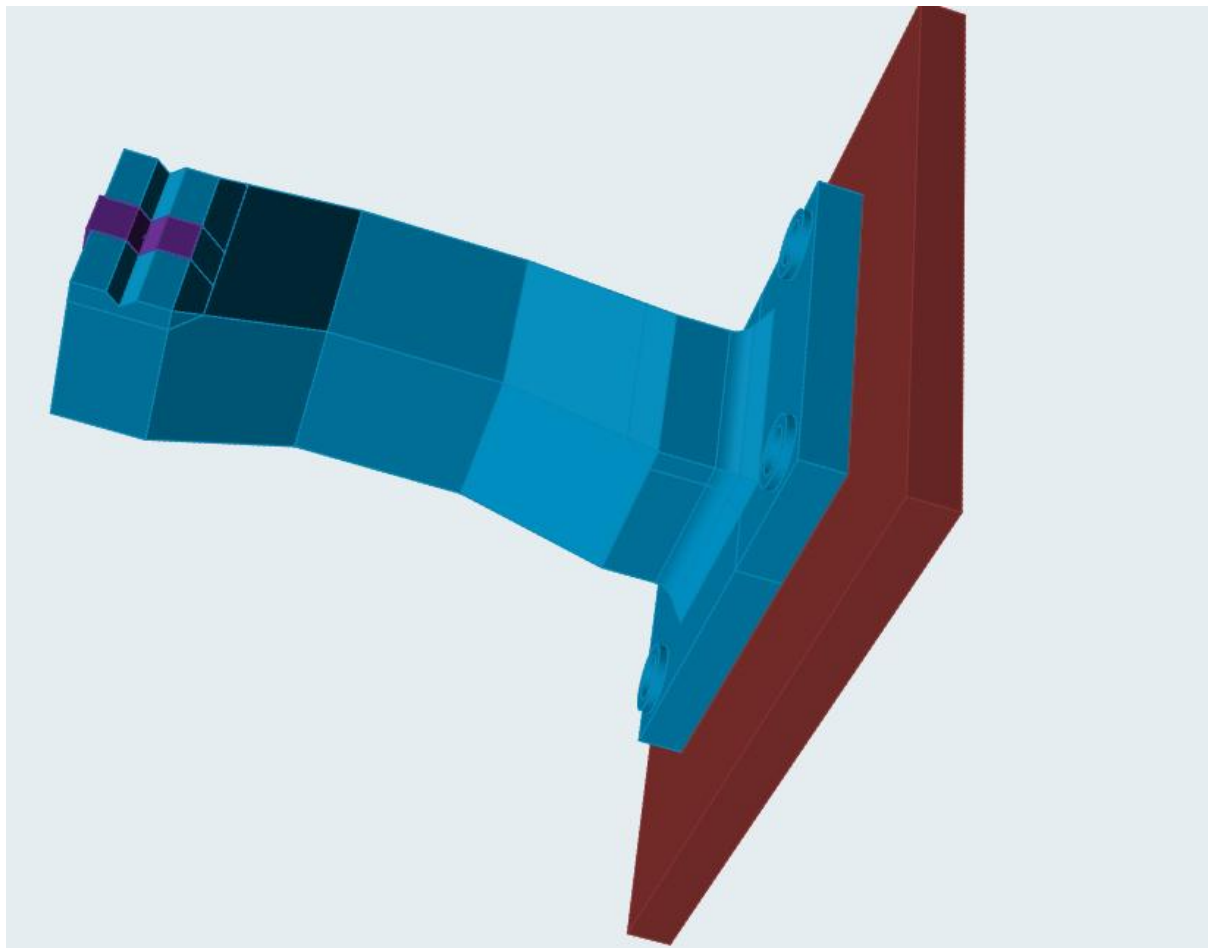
Převedení součásti ze SolidWorksu do Altair Inspire
